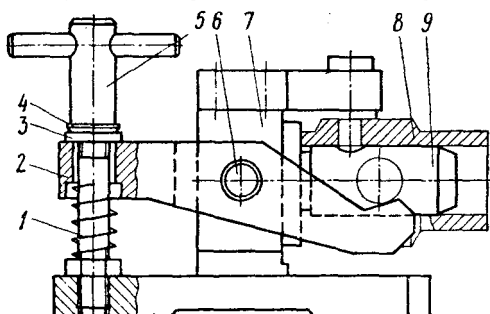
Приспособление для обработки отверстий в деталях технологического ряда ВЦ-01
